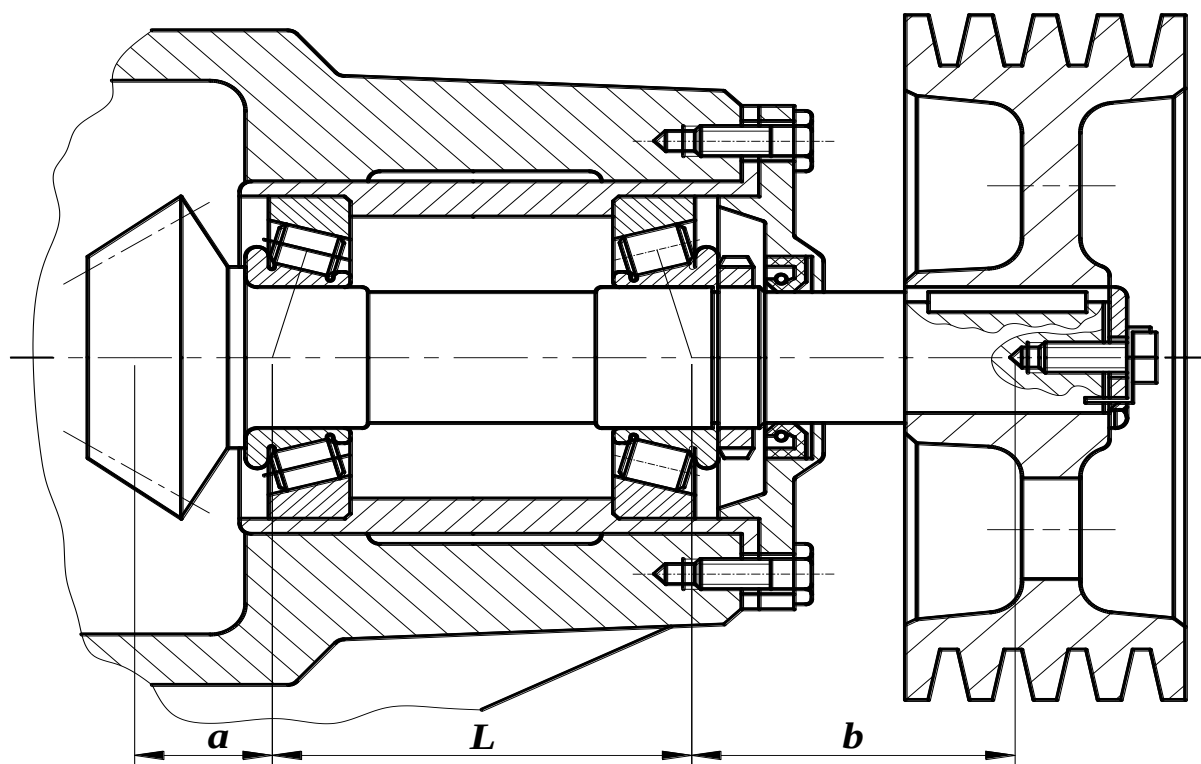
Входной вал конического редуктора со шкивом
